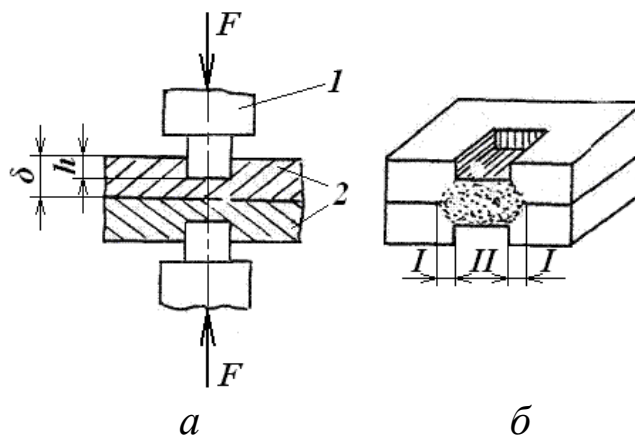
Схема сварки (а) и вид соединения (б): 1 – пуансоны; 2 – детали; I – внутренняя зона; II – периферийная зона.
